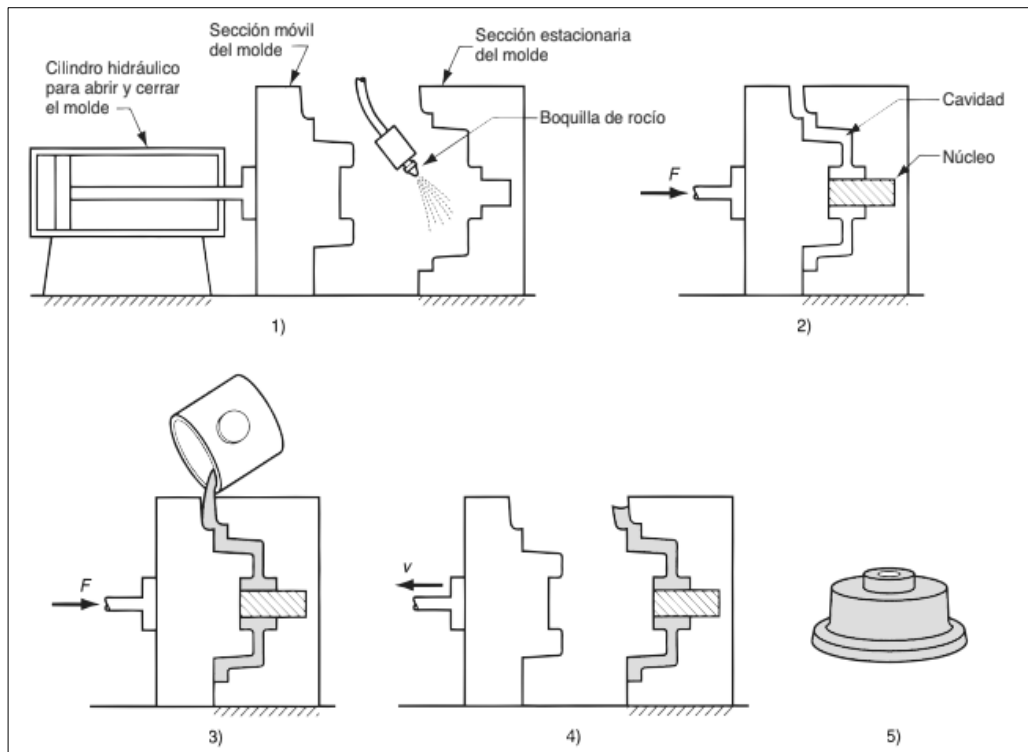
“Etapas de fundido con moldes permanentes: 1) se precalienta y recubre el molde, 2) se inserta núcleos (si hay) y se cierra molde, 3) se vierte metal derretido en el molde y 4) se abre el molde. 5) La pieza terminada se presenta” Fuente: [14].
